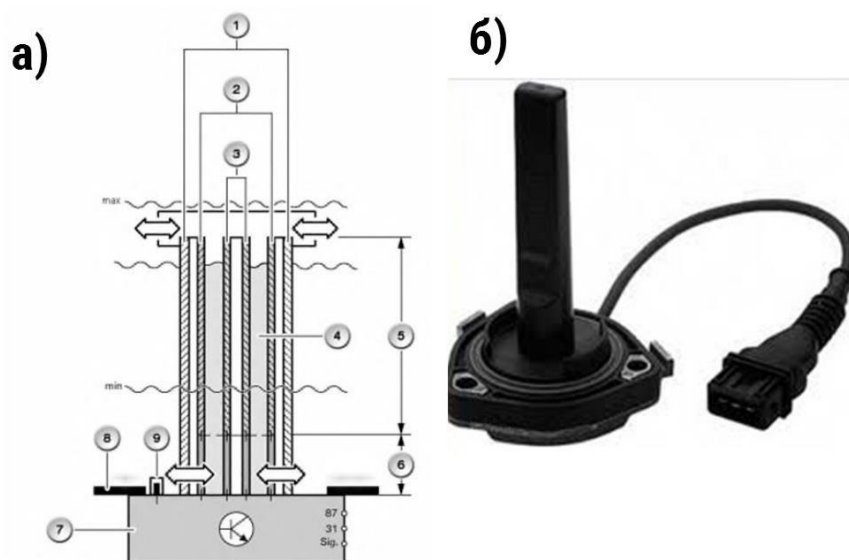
а) конструкція датчика стану оливи; б) загальний вигляд датчика: 1 – корпус, 2 – зовнішня трубка, 3 – внутрішня трубка, 4 – олива, 5 – діапазон виміру рівня масла, 6 – діапазон виміру стану моторної оливи, 7 – електронний блок, 8 – картер, 9 – датчик температури.
